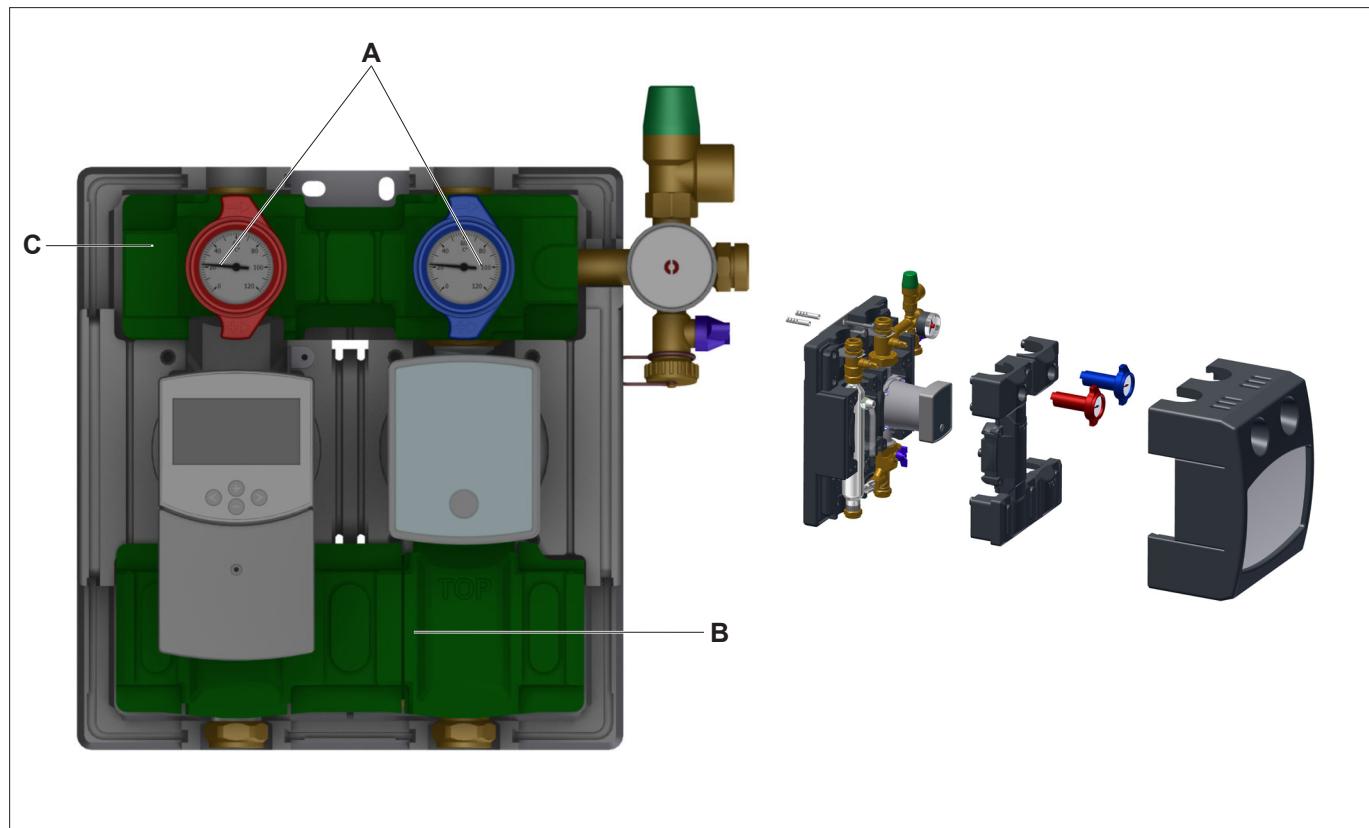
Isolierungen demontieren (dargestellt am Typ 8130 mit Entlüfterrohr und Regler)
